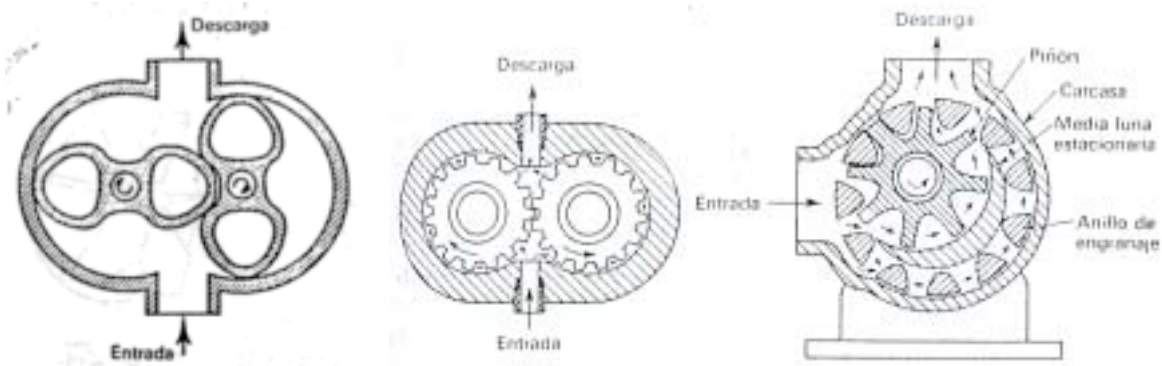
Bomba de lóbulos, de engranajes cilíndricos y de engranajes internos.
